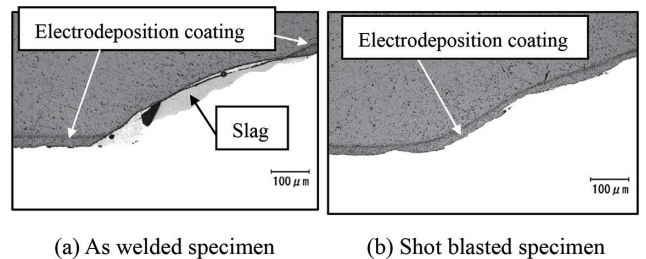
電着塗装後のアーク溶接止端部の断面 (440 MPa steel)
